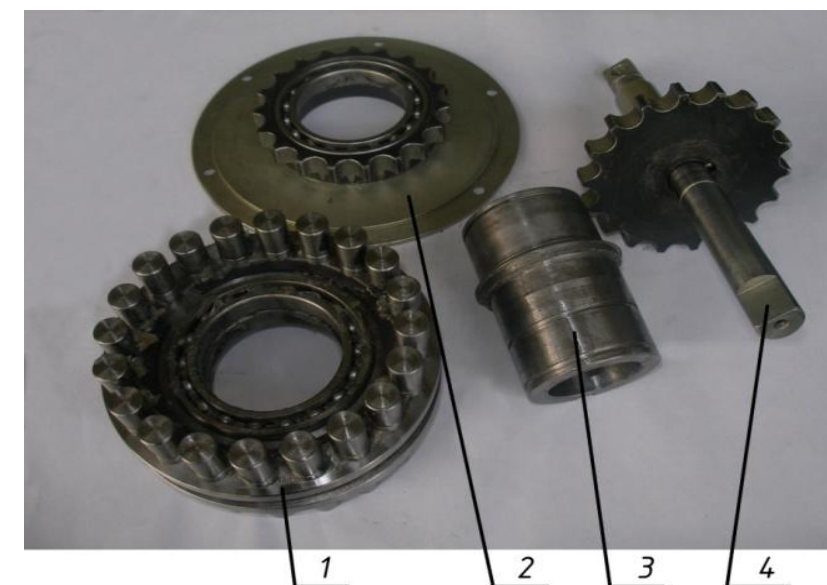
Вид основных деталей прецессионного редуцирующего механизма лебедки после проведения эксплуатационных испытаний: 1 – сепаратор с роликами; 2 – звездочка подвижная; 3 – косой вал; 4 – звездочка неподвижная с основным валом
